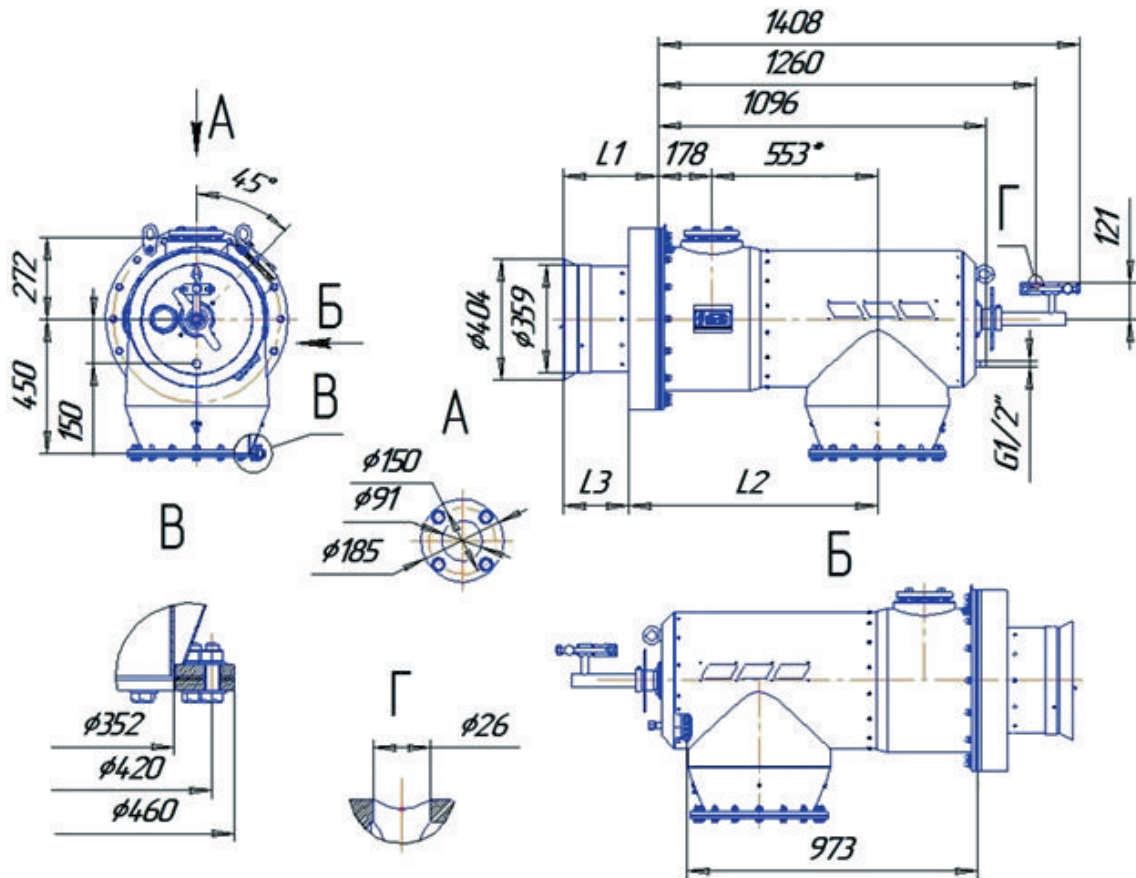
Габаритные и присоединительные размеры (исполнение 02, 03).
